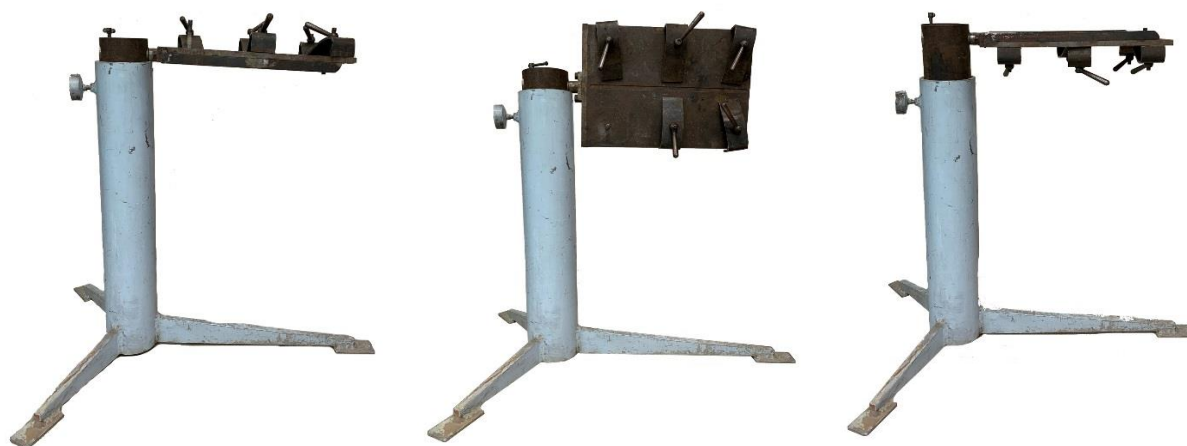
Контроль качества сварных швов лабораторной стойки
